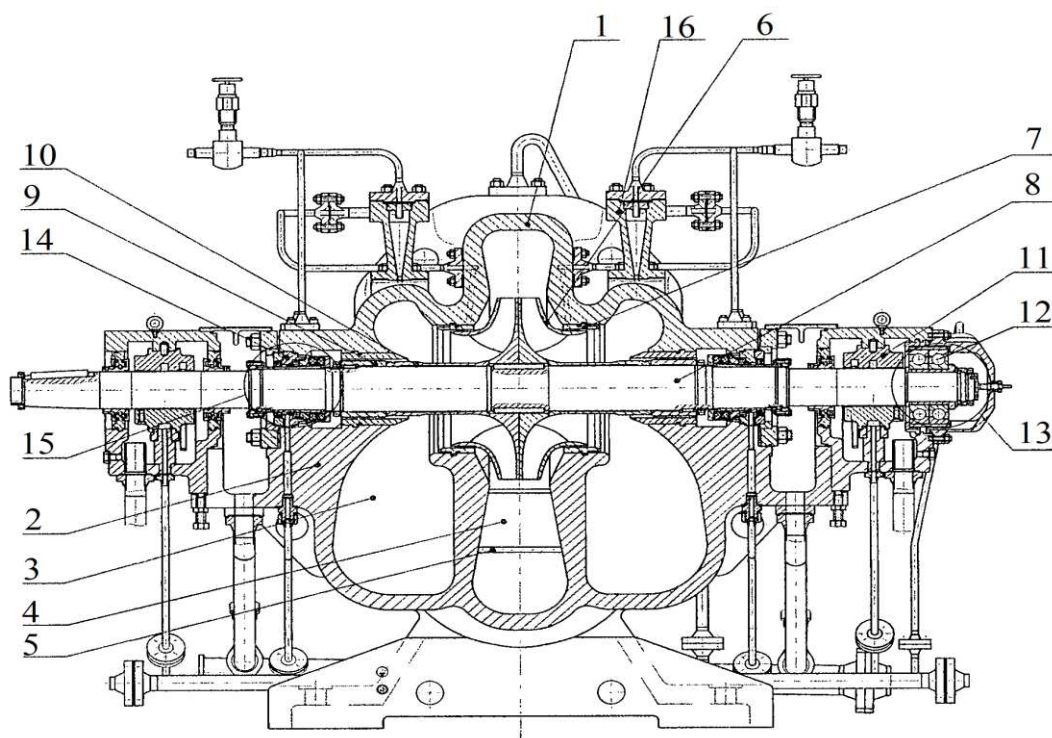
Разрез насоса HM10000-210: 1 – верхняя часть корпуса (крышка); 2 – нижняя часть корпуса; 3 – полуспиральный подвод;
